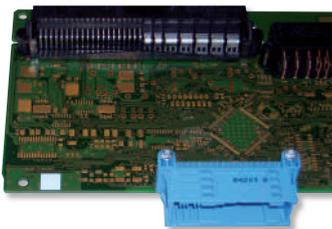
Ensamblaje conector PCB con tornillos PCB.
